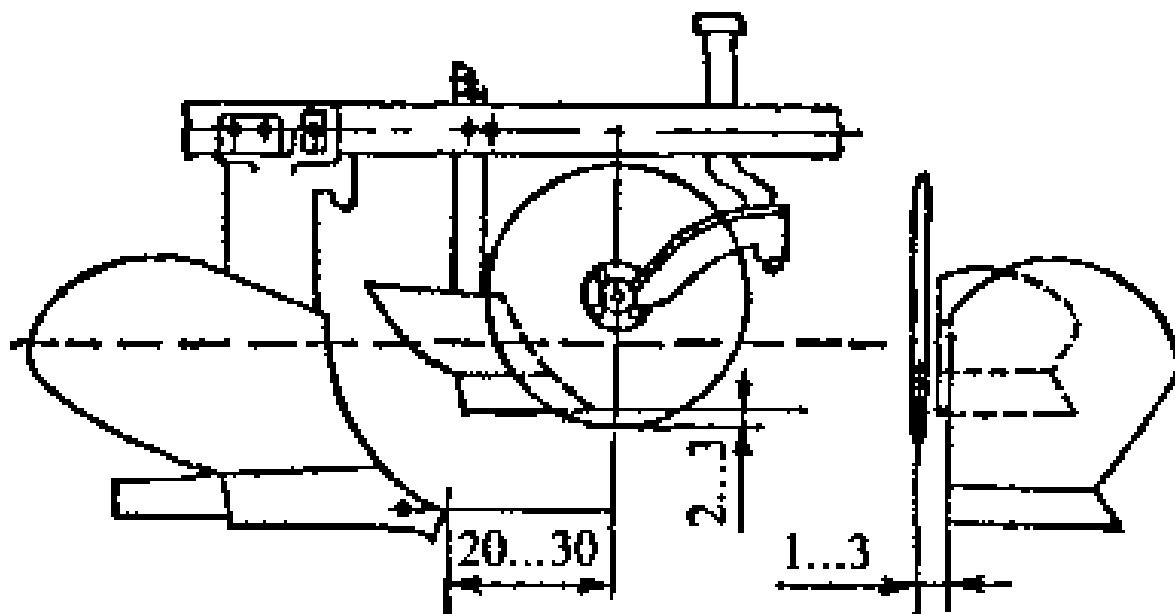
Схема установки предплужника и ножа на раме плуга.
